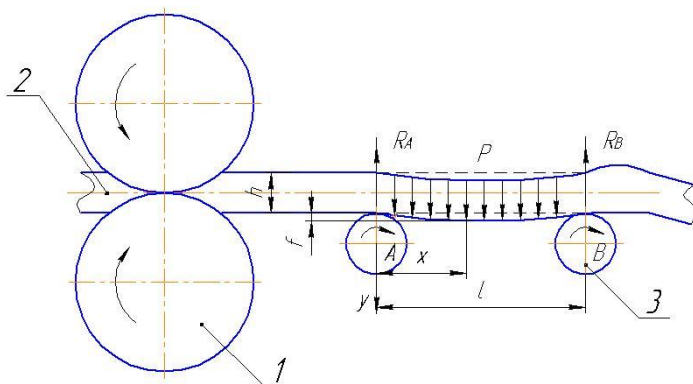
Розрахункова схема механізму подачі конвеєрної стрічки в зону різання: 1 – дискові ножі; 2 – стрічка; 3 – валки
